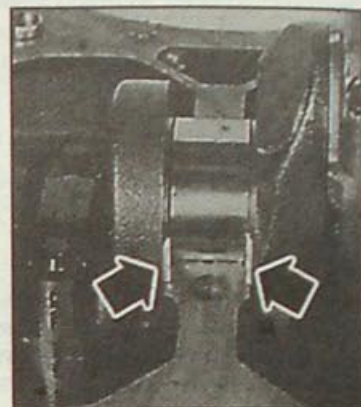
Расположение упорных полуколец регулировки осевого люфта коленчатого вала
